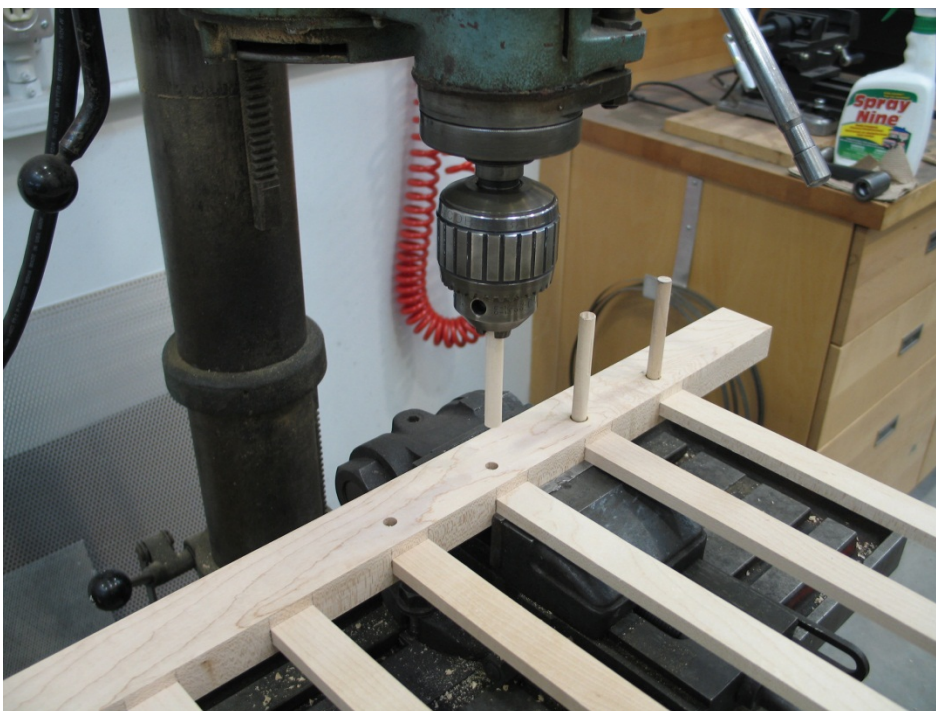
Fixation des assemblages de type tenon et mortaise sur les panneaux à barreaux avec un goujon par soudage rotationnel.
